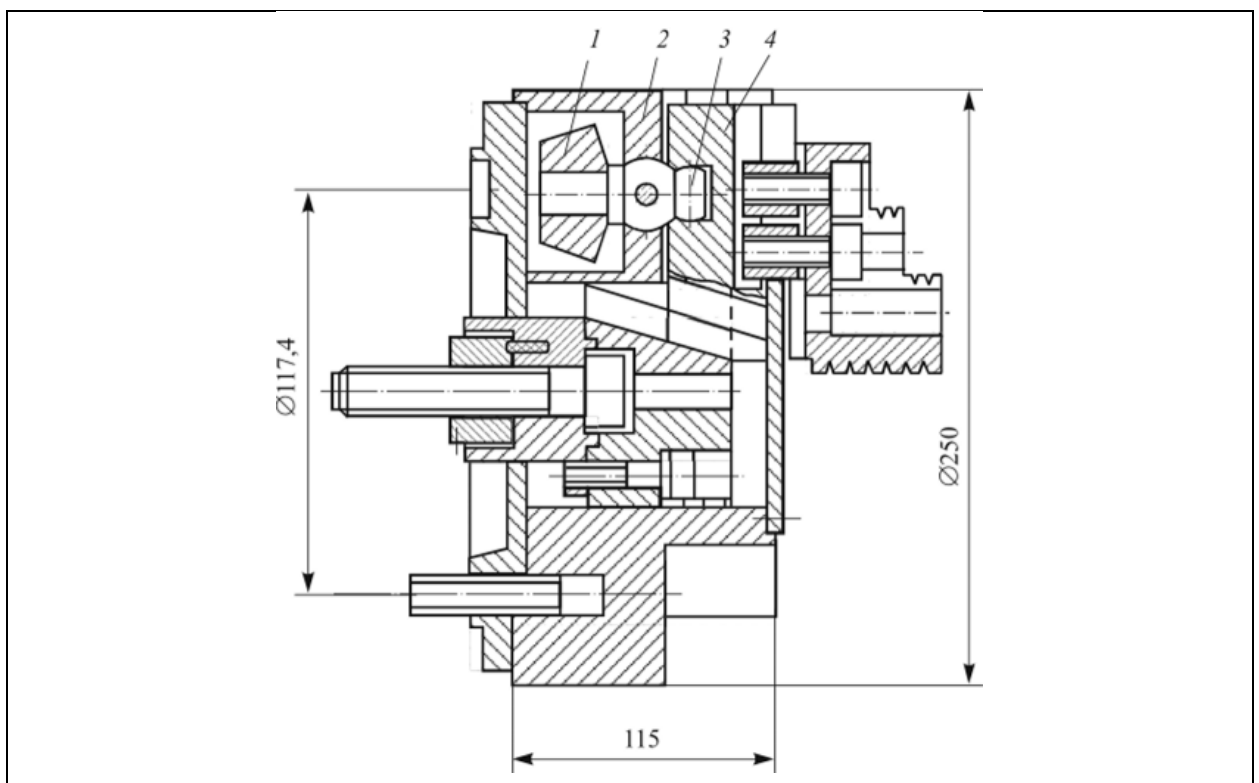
Самоцентрувальний клиновий токарний патрон для оброблення з великими частотами
